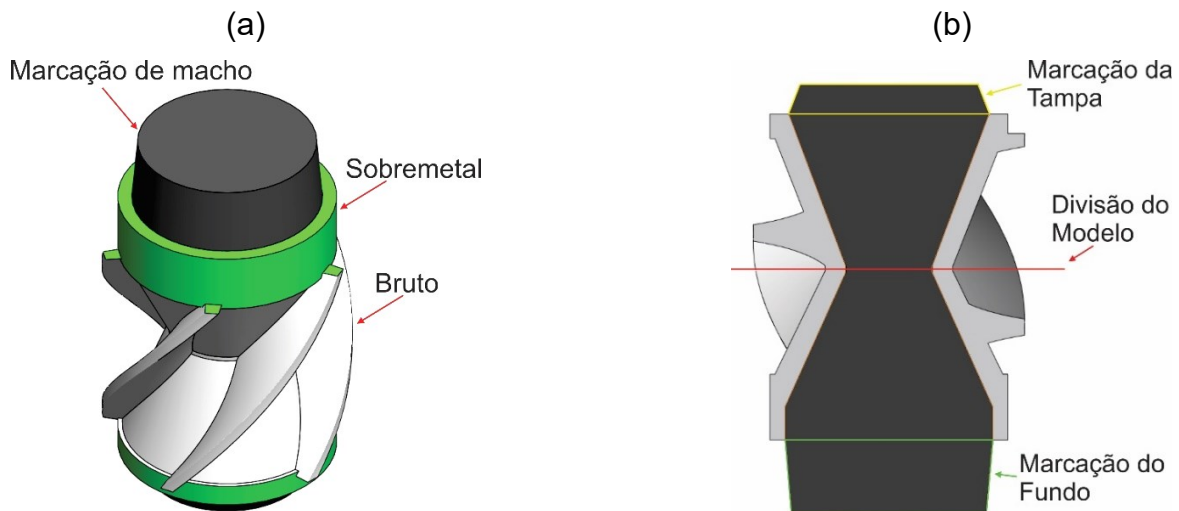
(a) Vista Isométrica; (b) Vista em Corte (Autor, 2020)
